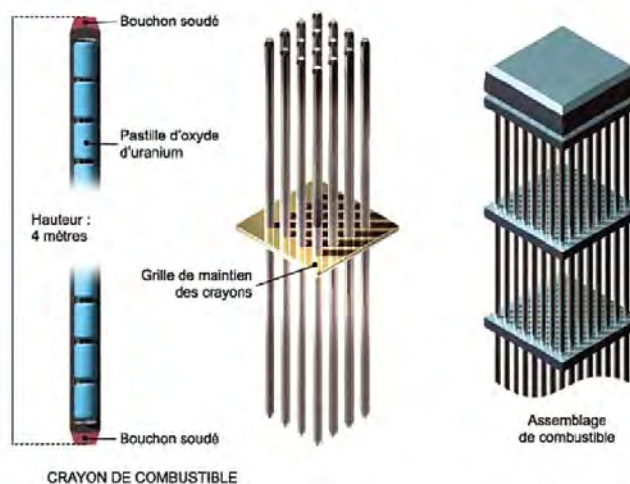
Schéma d'un crayon et d'un assemblage combustible [2].
